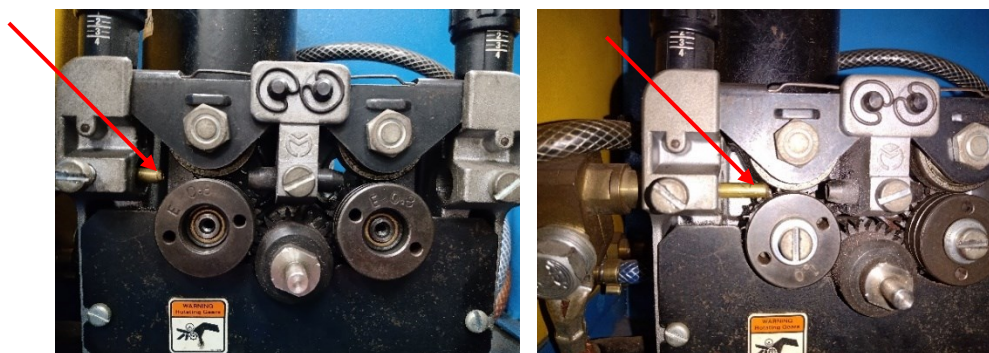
Ajuste do bico guia de arame de solda. (Autor).
